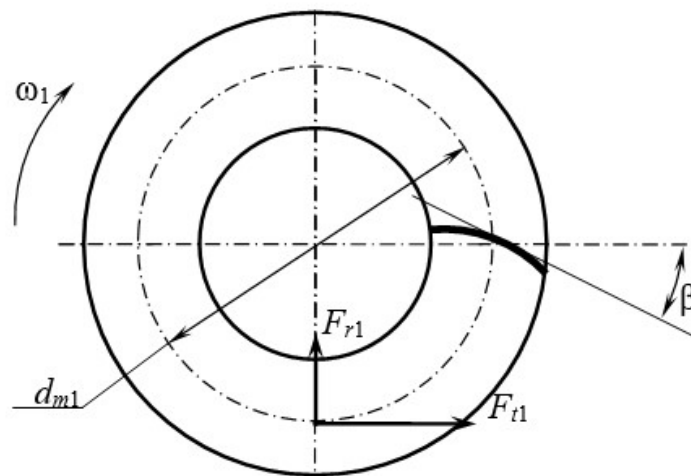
Коническая шестерня с круговым зубом (вид со стороны вершины конуса)
